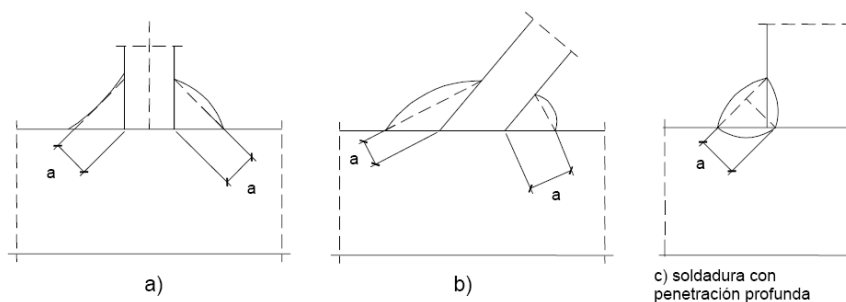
Soldadura en ángulo. Espesor de garganta
